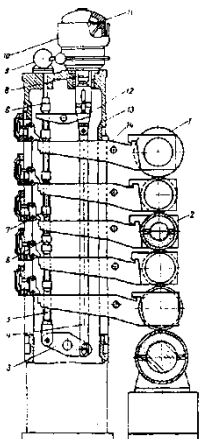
Машинний каландр: 1 — металеві вали; 2 — корпус підшипників;
